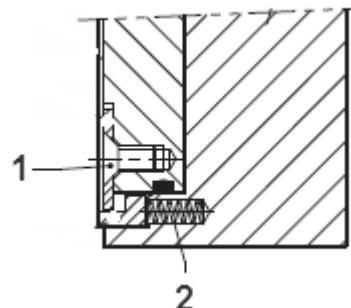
Revolverscheibe Seitenansicht M4x8 Zylinderschrauben und Feder
